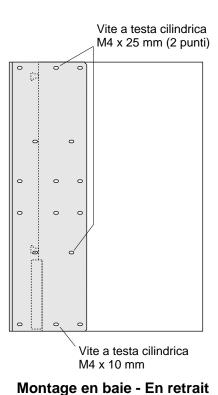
Installazione delle staffe di montaggio su un telaio alimentazione Adept PA-4
